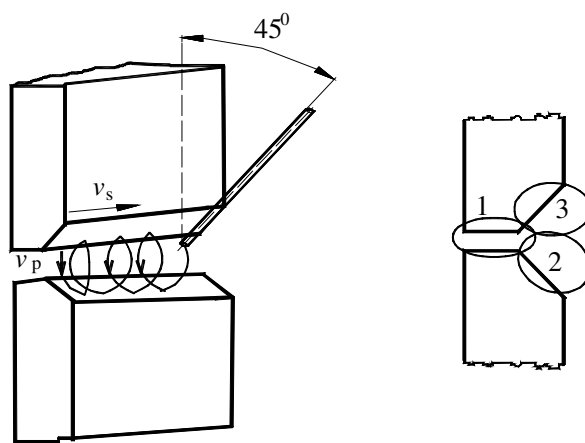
Poziția electrodului și mișcarea de pendulare la sudarea orizontală în plan vertical (sudarea în cornișă):
